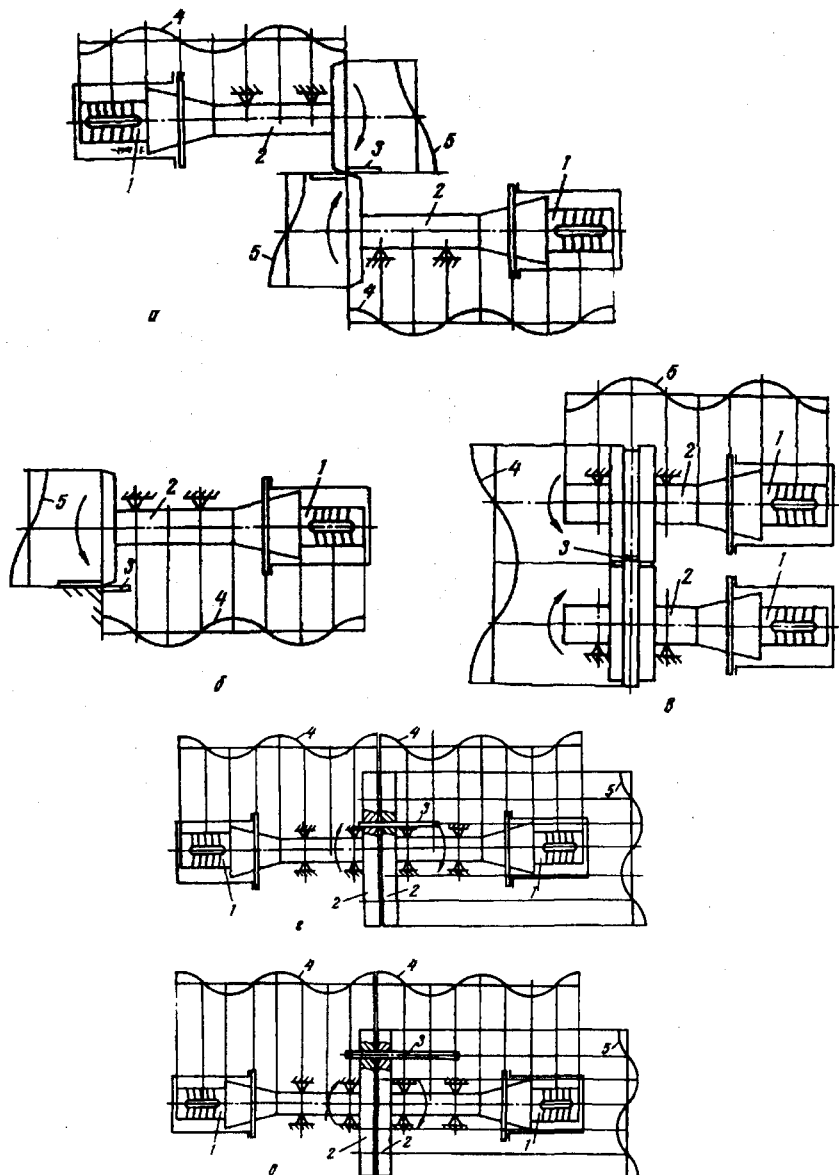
Ультразвуковые ножницы для резки листового и сортового материала: *а, б* – дисковые ножницы; *в* – роликовые ножницы; *г, д* – устройства для резки сортового металла (1 – преобразователи продольных колебаний; 2 – валки-инструмент, выполненные в виде излучателей радиальных колебаний; 3 – заготовки; 4 – эпюра продольных смещений; 5 – эпюра радиальных смещений)
